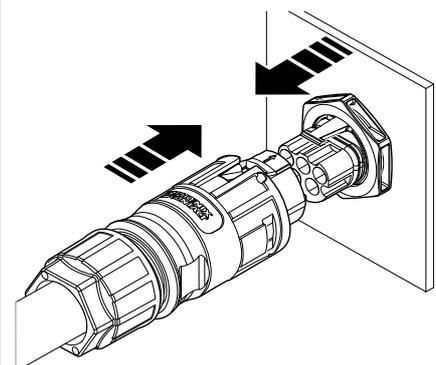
AC-Steckverbinder mit dem Gerätesteckverbinder einrasten.
